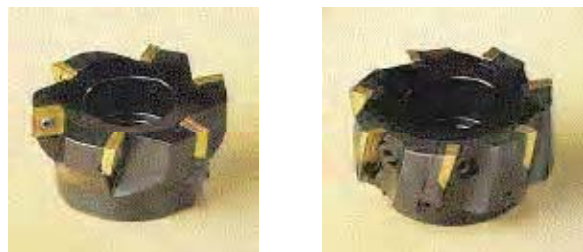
"Катушечные" фрезы для обработки алюминия и магниевых сплавов
